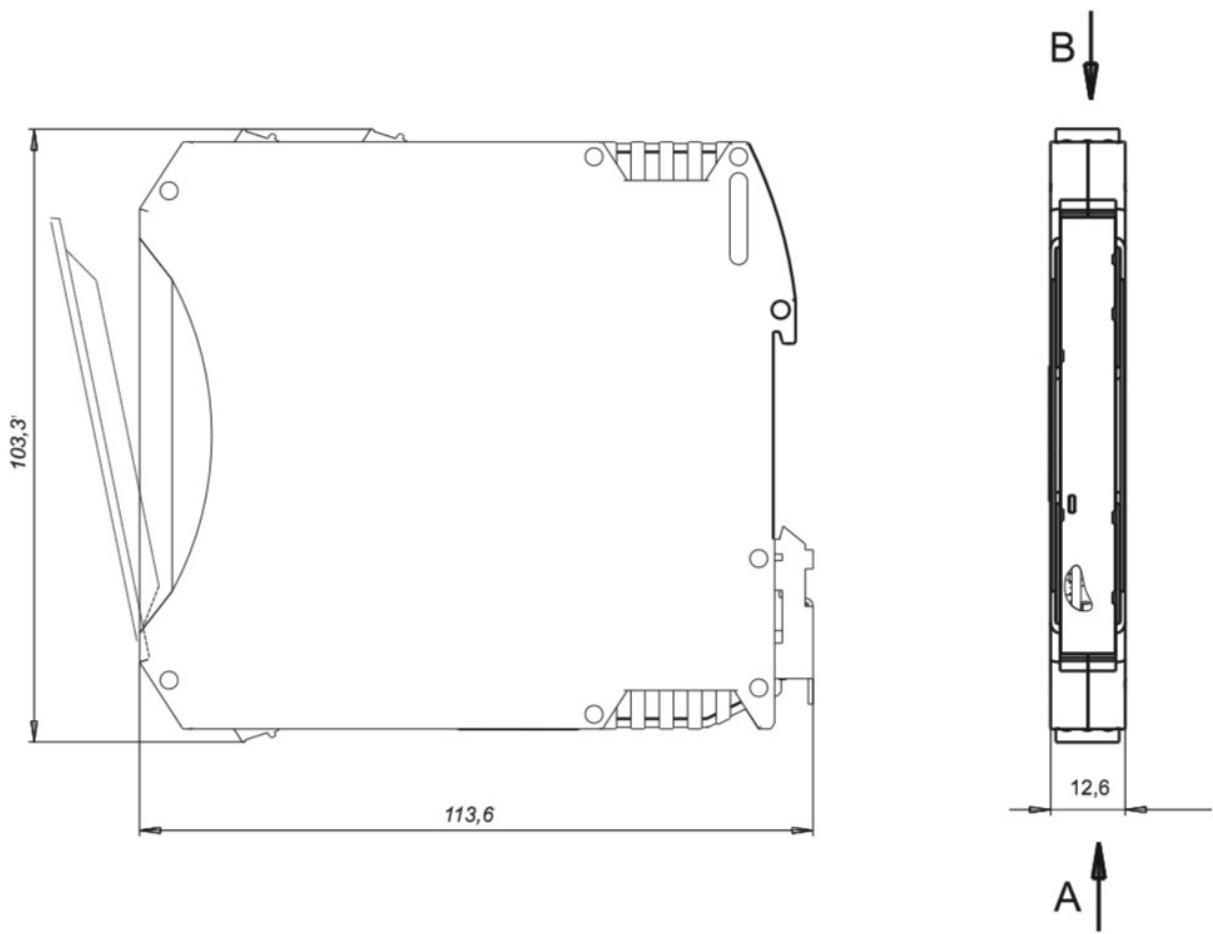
Внешний вид и габаритный чертеж барьера искрозащиты ET A 151
